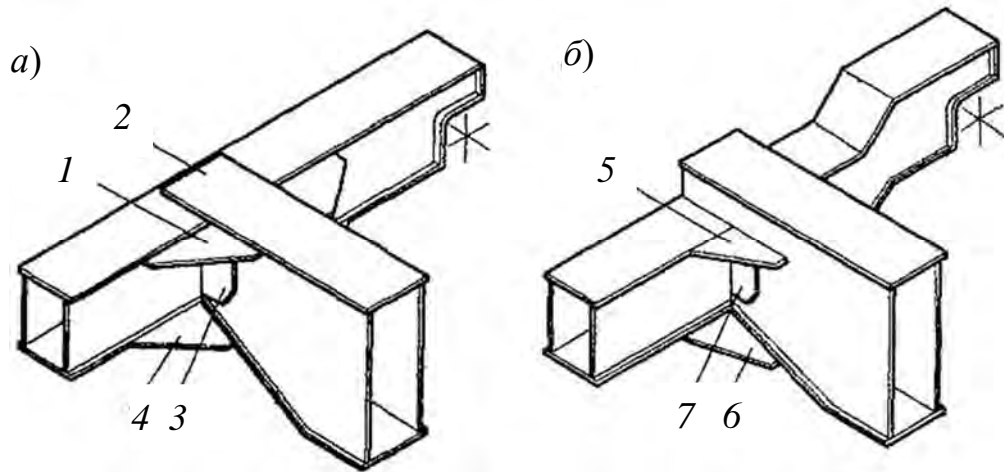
Узлы примыкания пролетных балок к концевым: *а* – с расположением верхних поясов балок на одном уровне; *б* – с зубом пролетной балки; 1 – угловые косынки; 2 – верхний пояс; 3, 7 – фасонки (укрепляющие пластины); 4 – выпуклые листы; 5 – укрепляющие ребра; 6 – отогнутые фасонки
